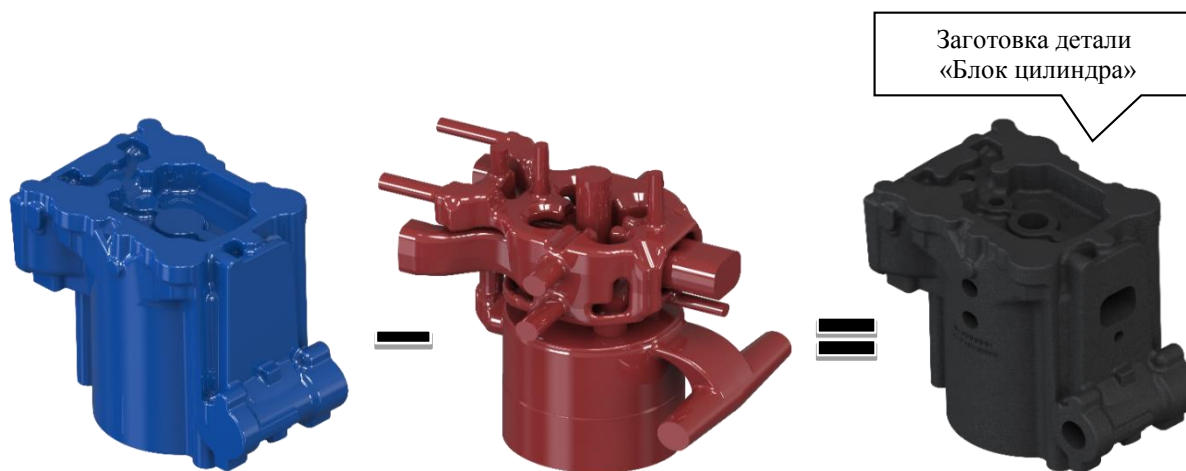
Компоновка модели заготовки детали «Блок цилиндра»
